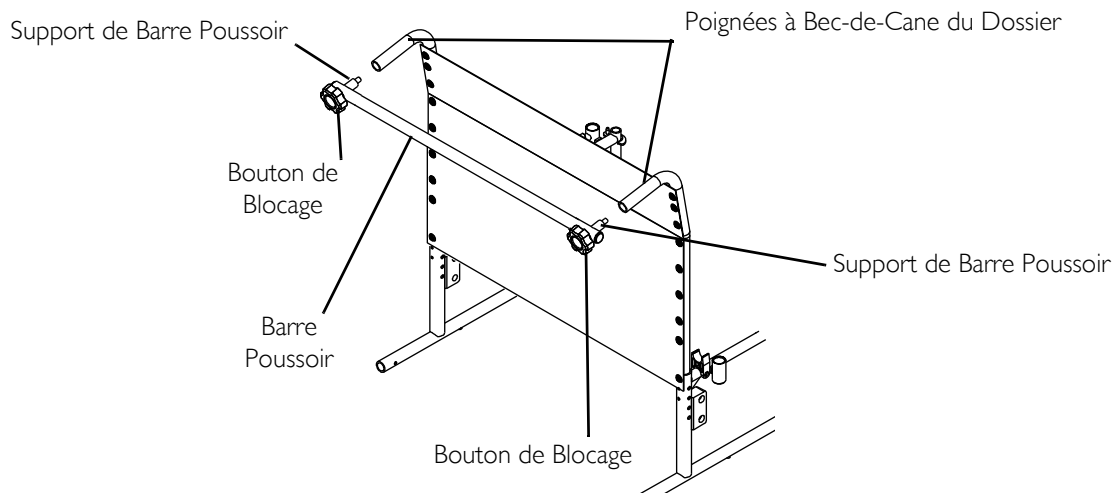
Installer/Enlever la Barre Poussoir
